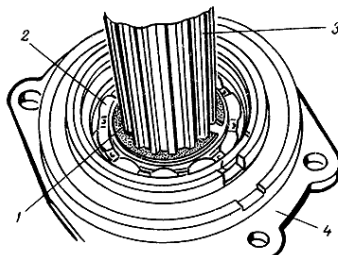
Снятие стопорного кольца подшипника первичного вала:
